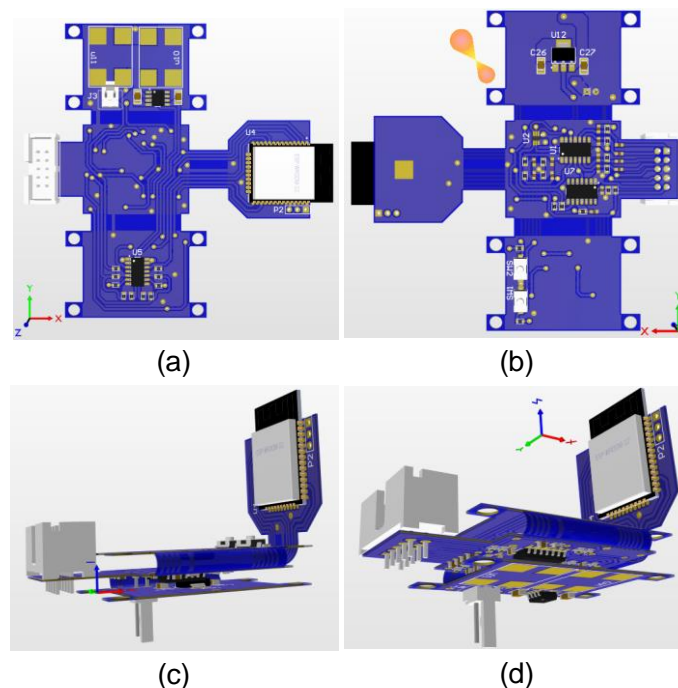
PCB *flex-rigid* desenvolvida (a) vista superior (*top*) (b) vista inferior (*bottom*) (c e d) duas perspectivas da PCB dobrada.
